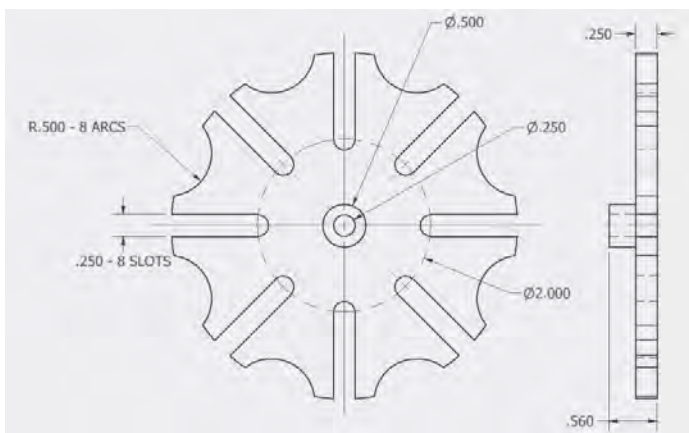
figura construida en IPS y con un valor de extrusión de 1 Pulgada y la pieza se realiza en plano planta.
